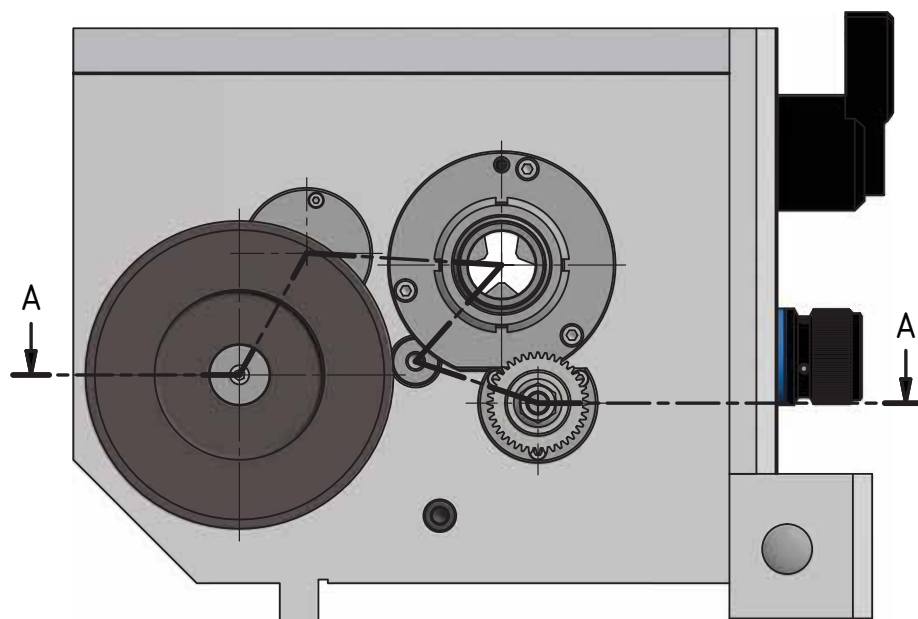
Getriebe Spindelstock 2-6 - Headstock gear 2-6
